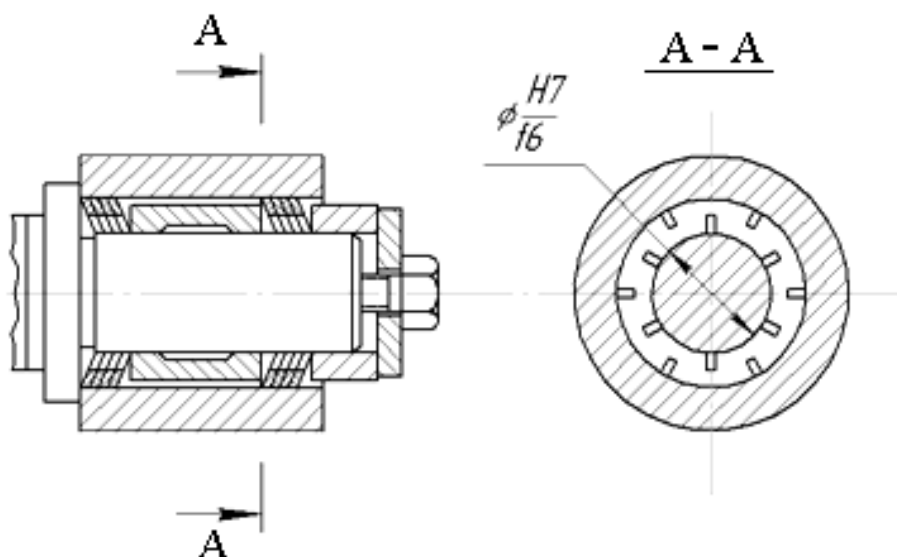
Установка заготовок на оправці з тарілчастими пружинами.
